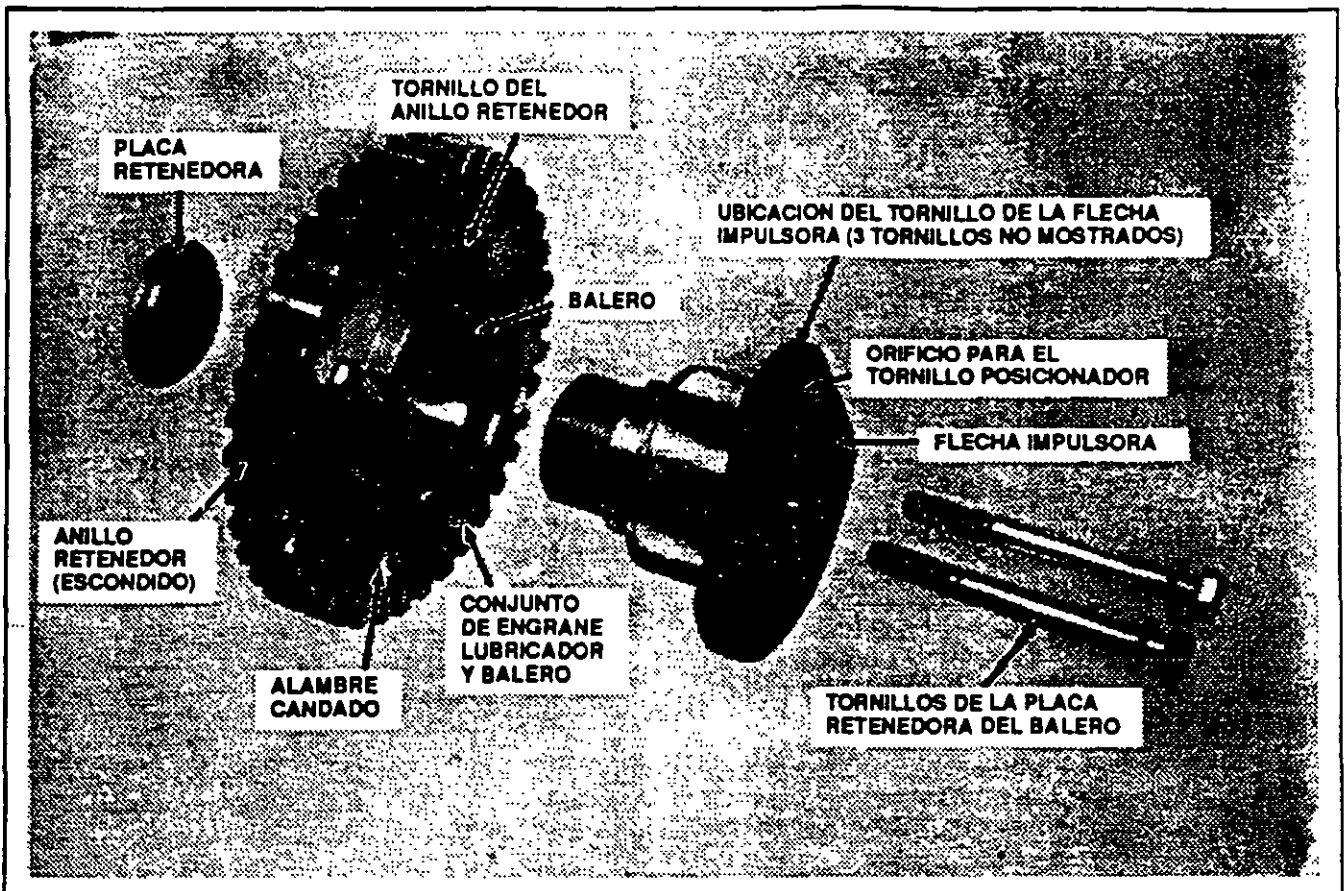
CONJUNTO DE ENGRANE LUBRICADOR (VISTA EN PARTES). E-24248-S
